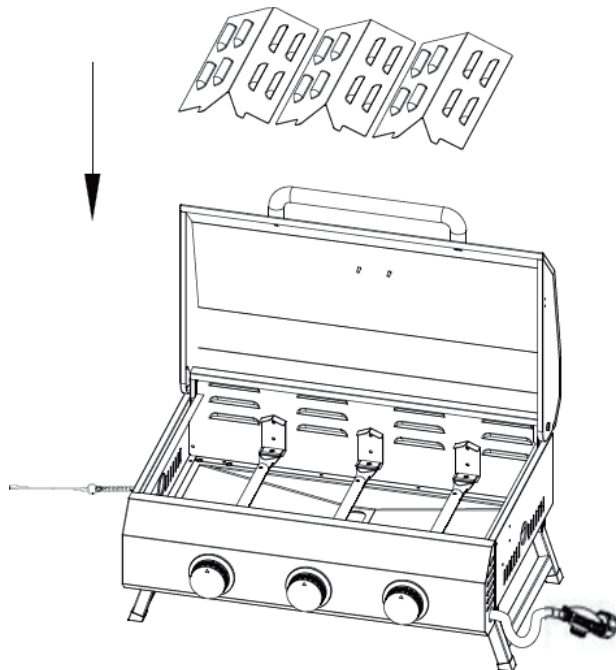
installer le gril sur le foyer comme montré ci-dessous.
